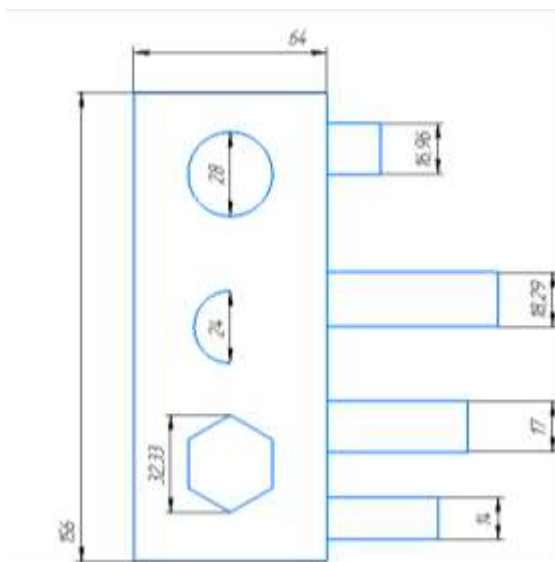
Простановка размеров с использованием инструмента «Авто-размер»
